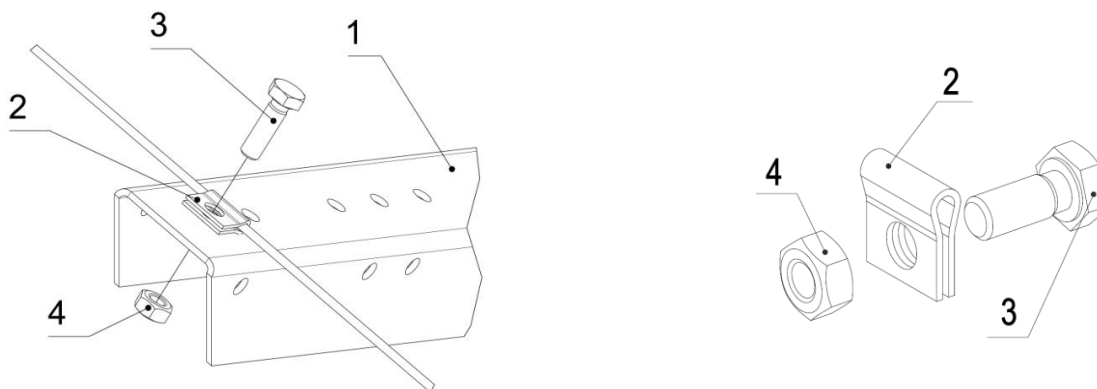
Установка фиксатора проволоки (1 – штанга, 2 – фиксатор проволоки, 3 – болт М6х35 DIN 933, 4 – гайка М6 DIN 934).
